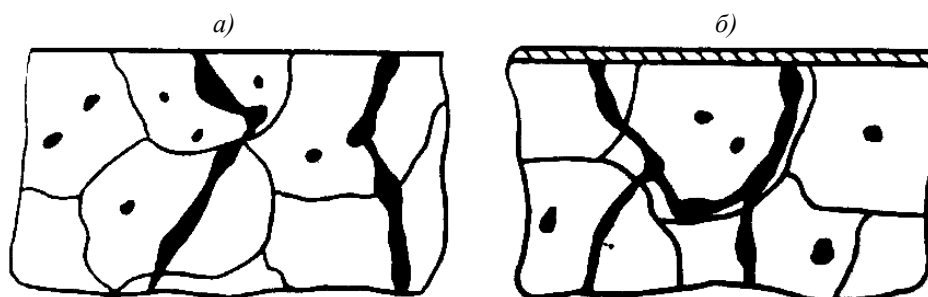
Схема запрессовки сквозных дефектов в отливке:
